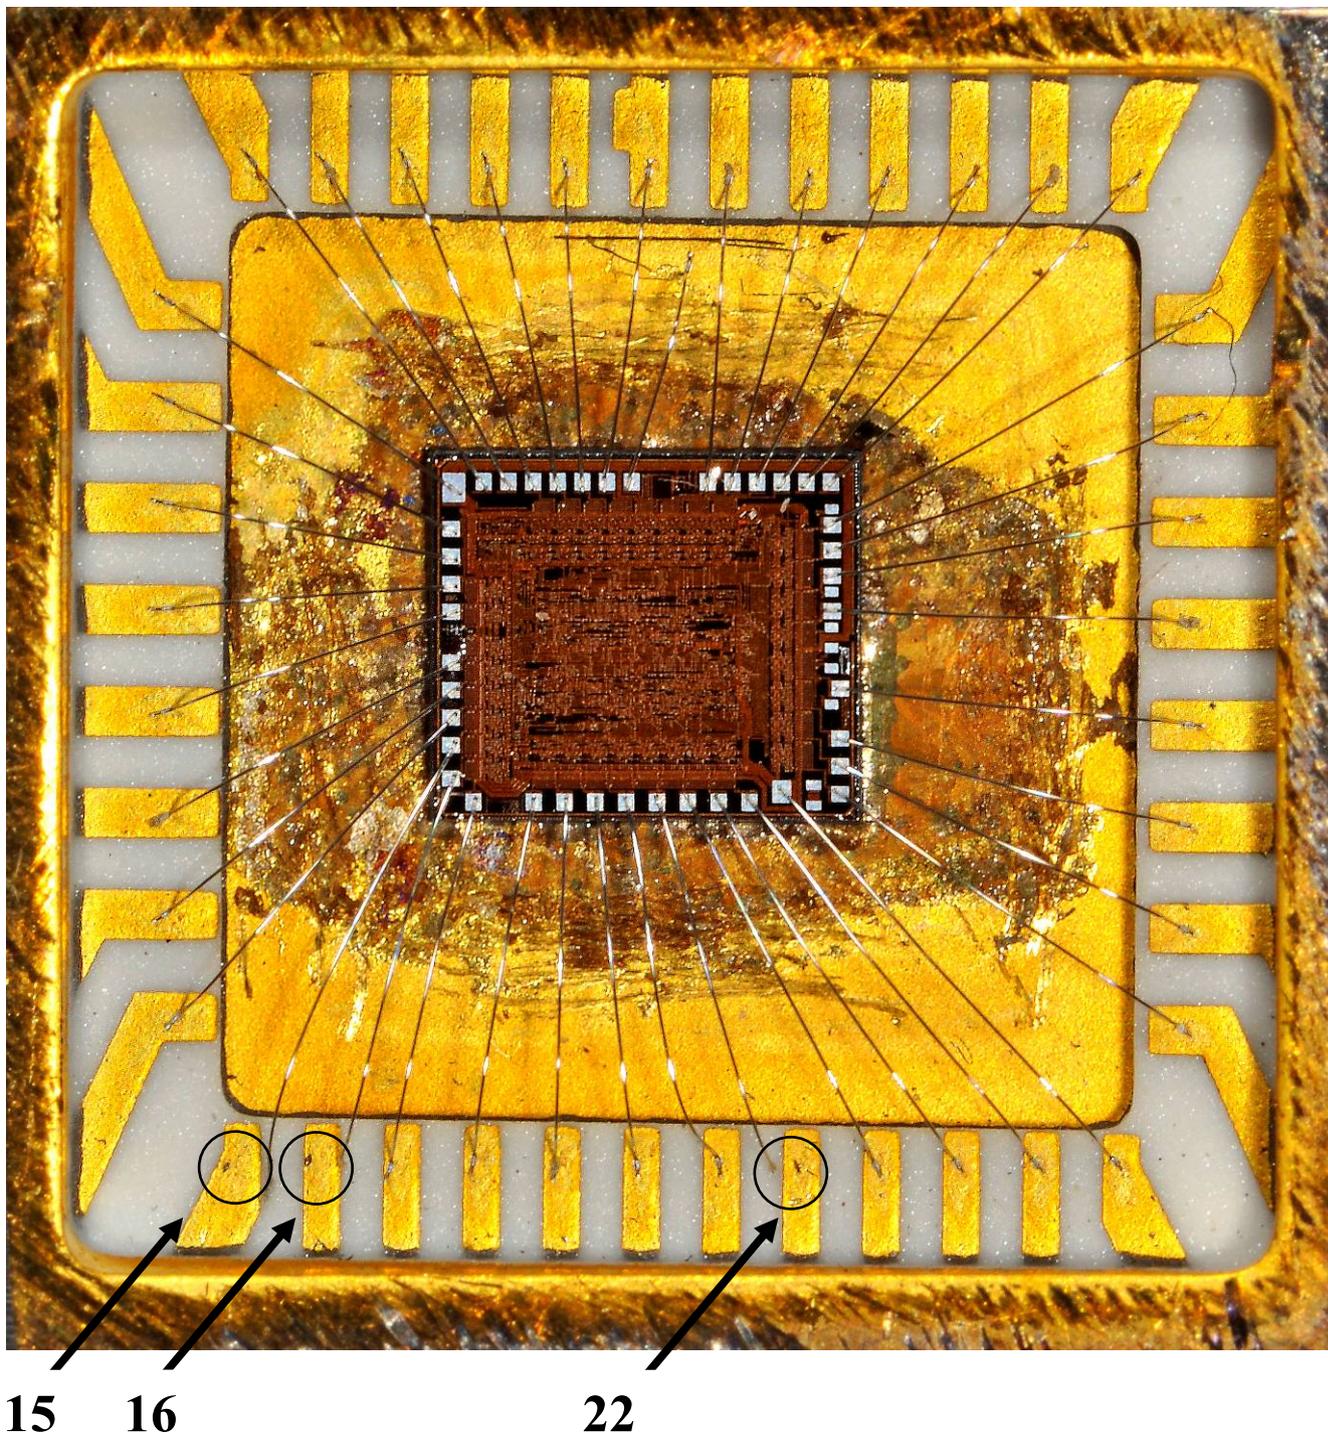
Внешний вид интегральной микросхемы 580ВВ55 с нарушенными сварными соединениями на выводах № № 15, 16, 22 малых траверс (нарушенные сварные соединения указаны стрелками).
